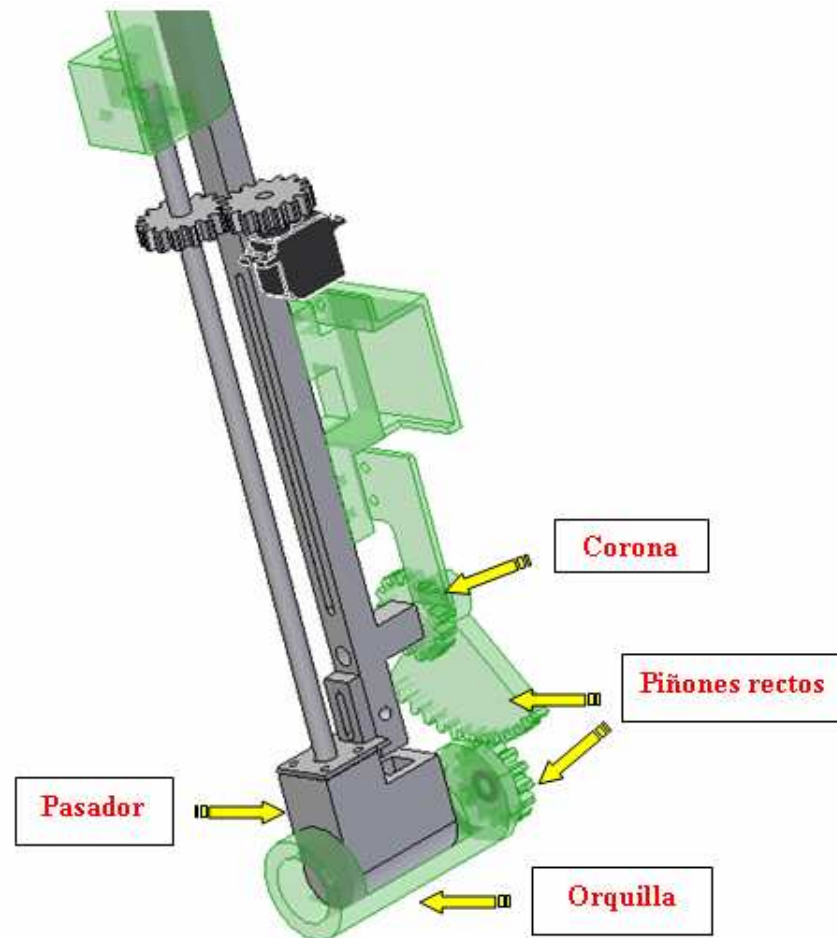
Pasador acoplado en orquilla y bujes de fricción.
